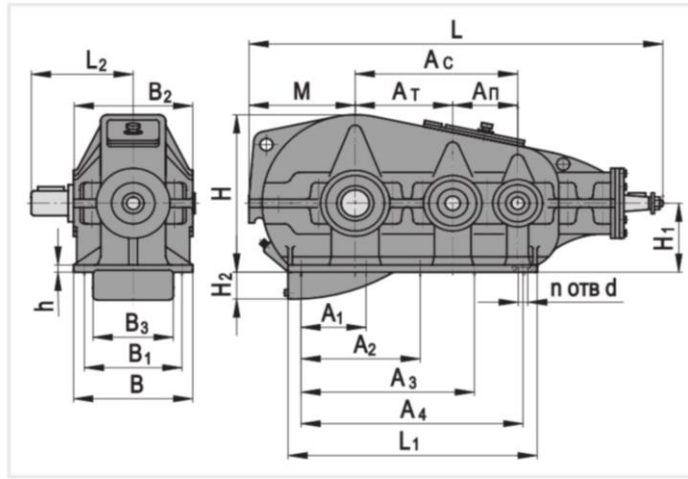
Схема редуктора КЦ1-500-6,3-41-УЗ
